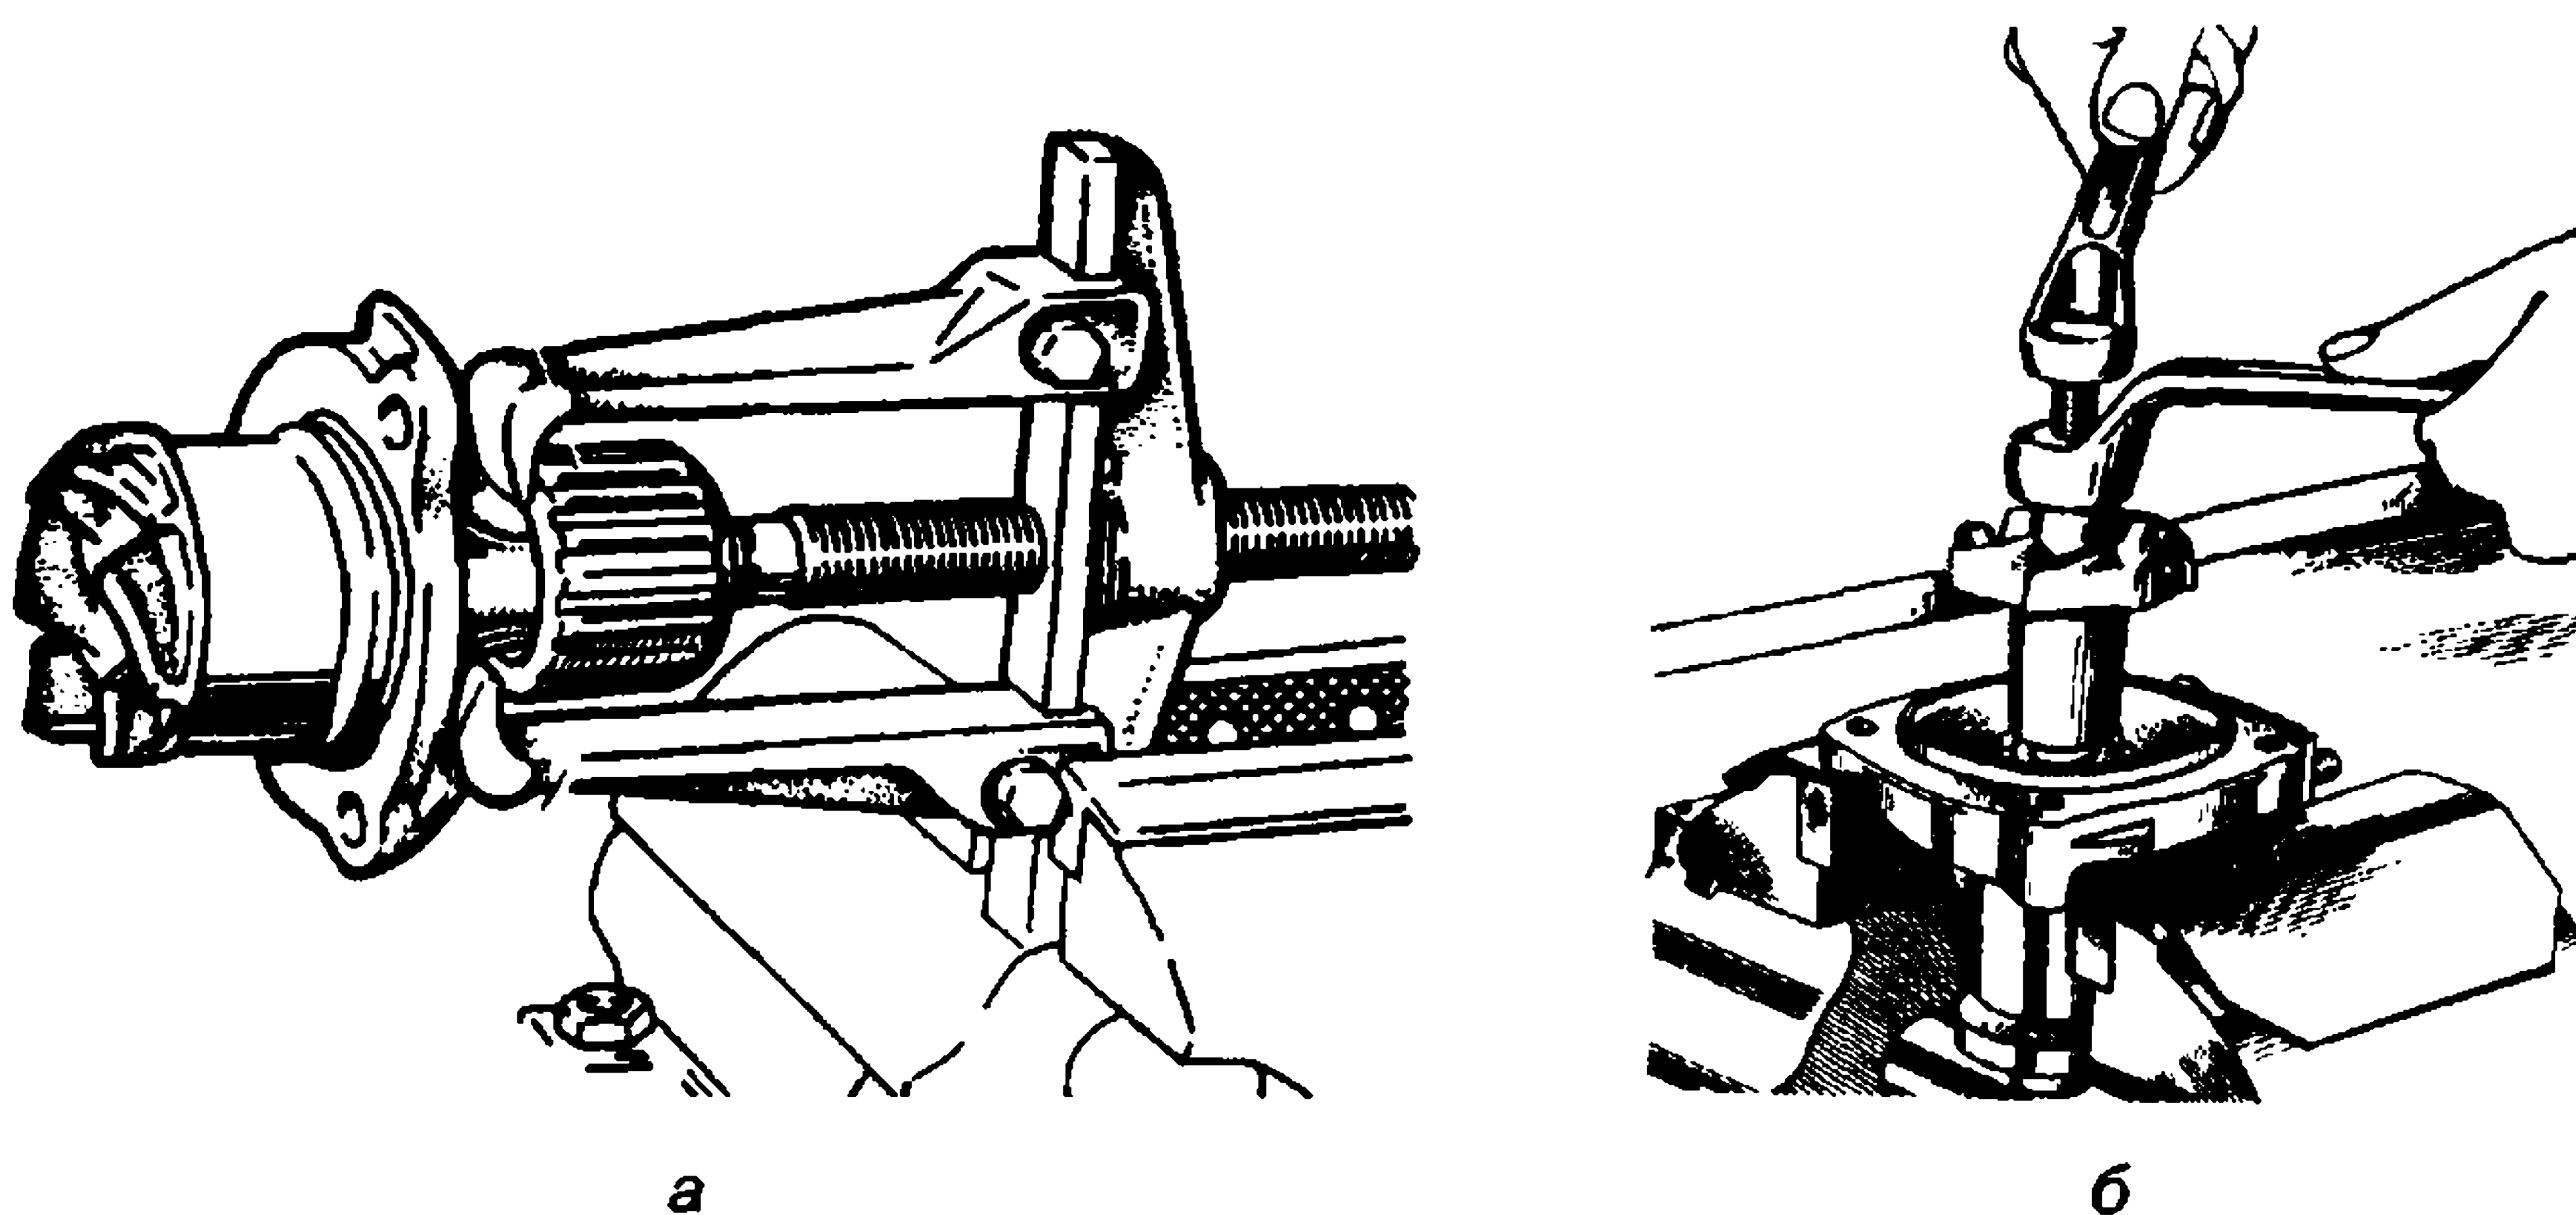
Снятие ступицы шкива (а) и выпрессовка крыльчатки (б)
